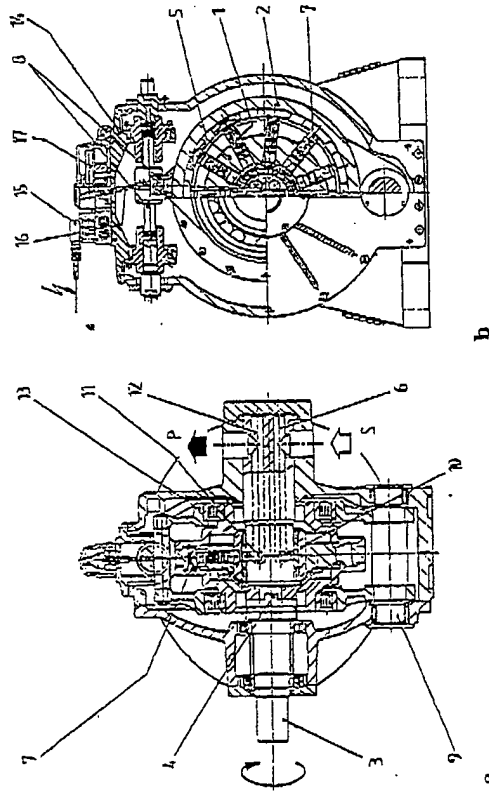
Radialkolbenpumpe, innen beaufschlagt (RX, Wepuko Hydraulik) mit elektrohydraulischer Stelleneinrichtung (Nr. 6) als Bauteil eines Verstellprogramms für die Pumpensteuerung. a Längsschnitt in Schwenkachse; b Querschnitt senkrecht zur Schwenkachse
